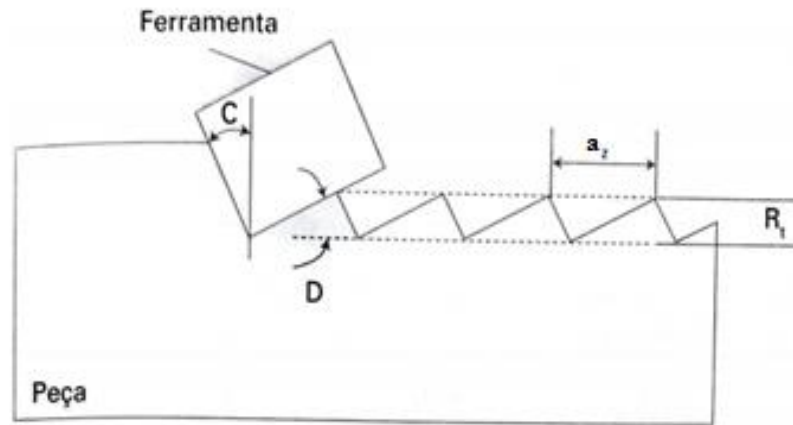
Perfil teórico de superfície usinada por fresamento frontal [24].
